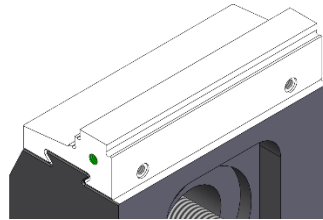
Spannbacke mit glatter Stufe Detailansicht
